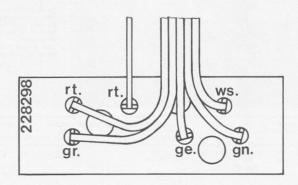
Abgleichpositionen und Lageplan der Steckverbindungen
